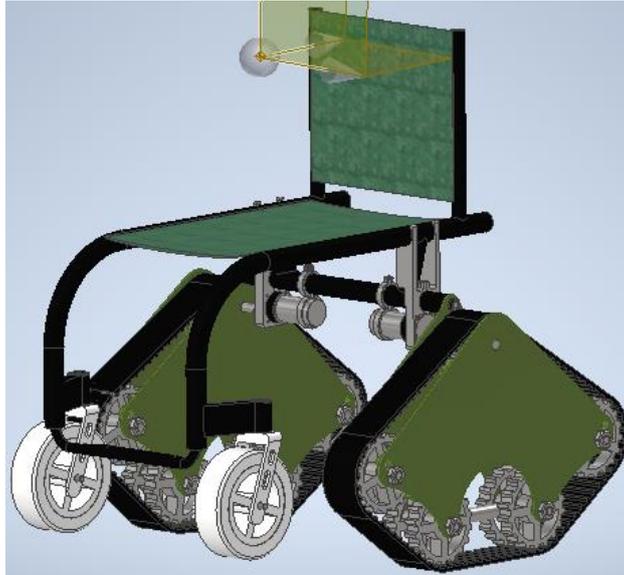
Soporte-placa de la parte interior y placa de la parte exterior, diseño sistema triangular- 2021
